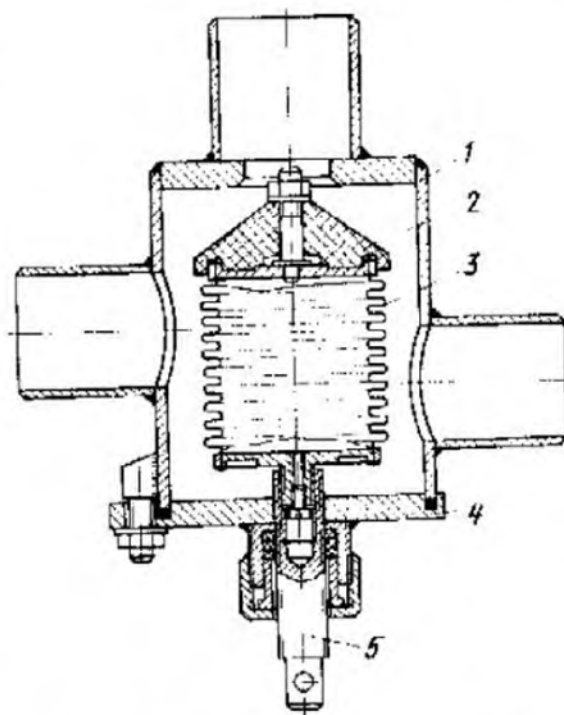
Регулятор Свердловскэнерго (ТК-6-10): 1 — корпус; 2 — клапан; 3 — чувствительный сильфон; 4 — фланец; 5 — регулировочный винт
